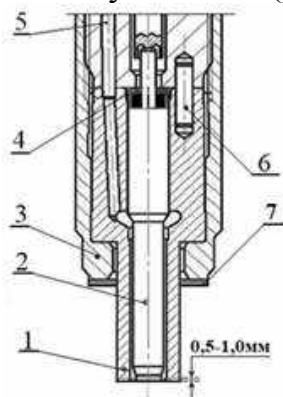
Адаптер: 1 – корпус фальш – розпилювача; 2 – голка розпилювача; 3 – гайка; 4 – фіксує герметизуючий елемент; 5 – корпус форсунки; 6 – установочний штифт; 7 – ущільнююча прокладка
